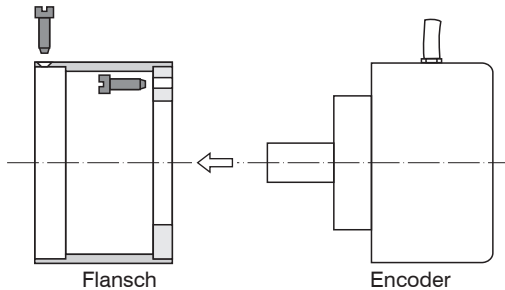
Montage von Flansch und Encoder, WDS-Z60
